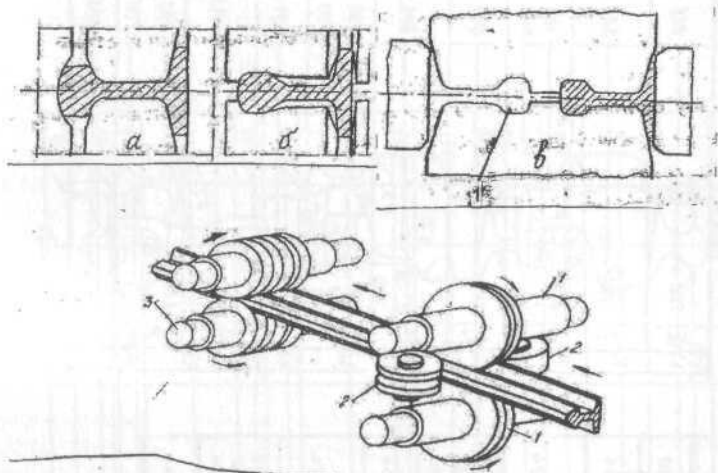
Схема прокатки рейок з використанням багатовалкових калібрів: а - універсальна чотиривалкова кліть; б - допоміжна двохвалкова кліть; в - чистова універсальна кліть з тривалковим калібром (1 - запасний калібр). Розташування клітей в лінії стана : 1,2 - горизонтальні і вертикальні валки універсальної кліті; 3 - допоміжна кліть з горизонтальними валяннями
